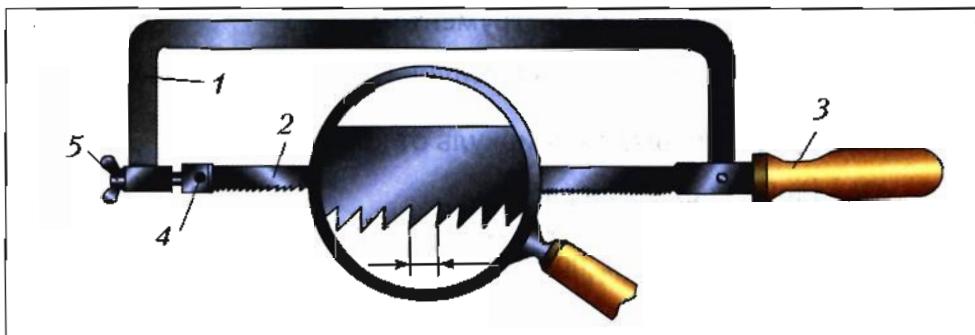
Устройство слесарной ножовки: 1 – рамка, 2 – ножовочное полотно, 3 – ручка, 4 – штифт крепления полотна, 5 – натяжная гайка
